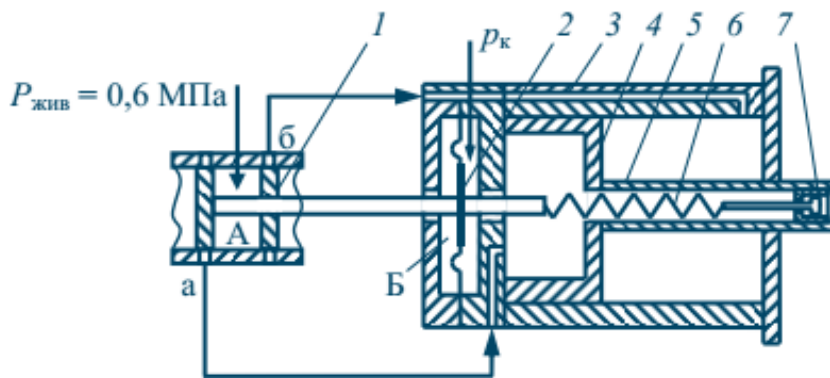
Пневмопоршневий привід: 1 – золотник, 2 – мембрана, 3 – циліндр, 4 – поршень, 5 – порожнистий шток, 6 – пружина, 7 – натяжний механізм
